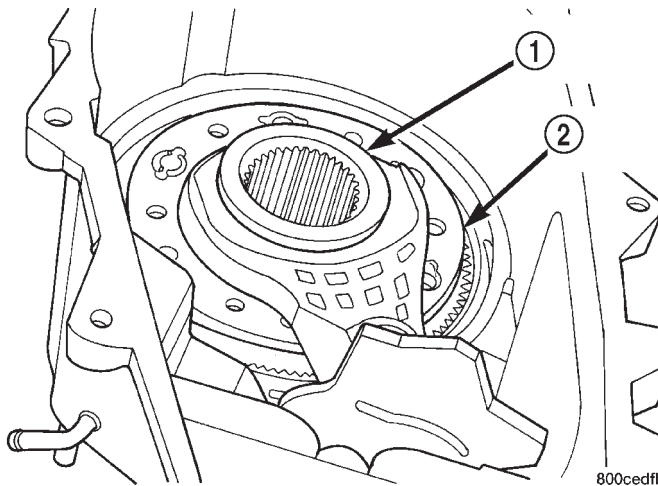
Instalación del conjunto de horquilla y manguito de la escala de posiciones
